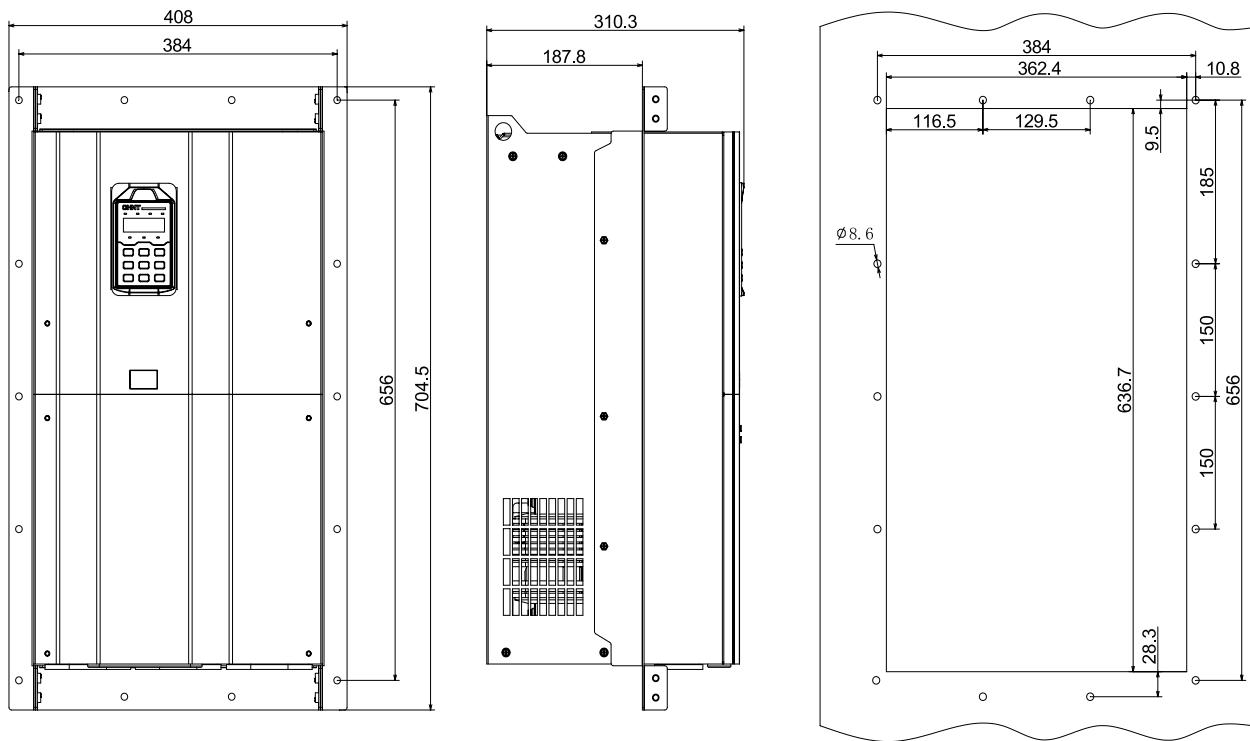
Комплект фланцевого монтажа для типоразмера Т8
